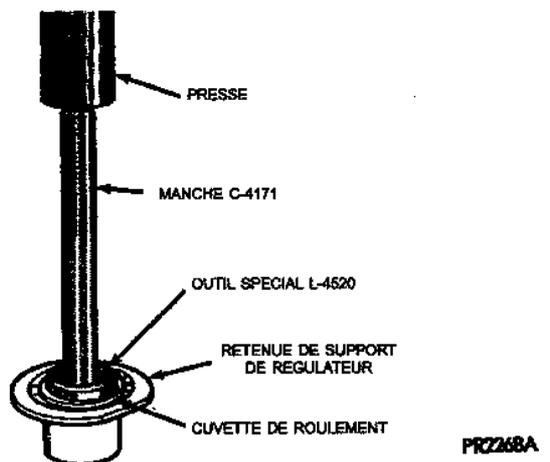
Pose de la cuvette de roulement de retenue du support du régulateur
